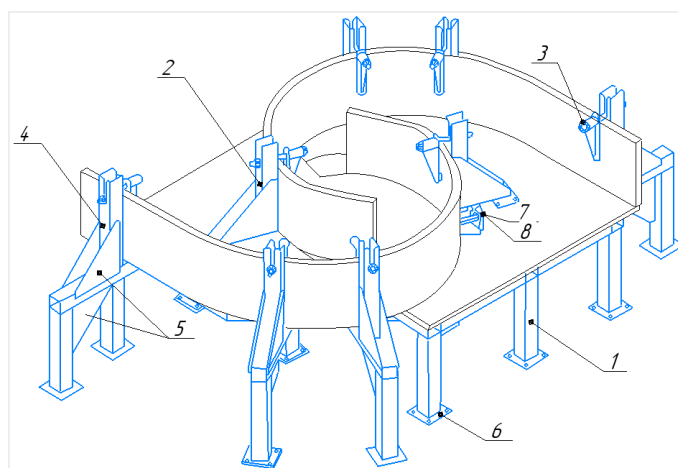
Специальное приспособление для сварки улиткового питателя
